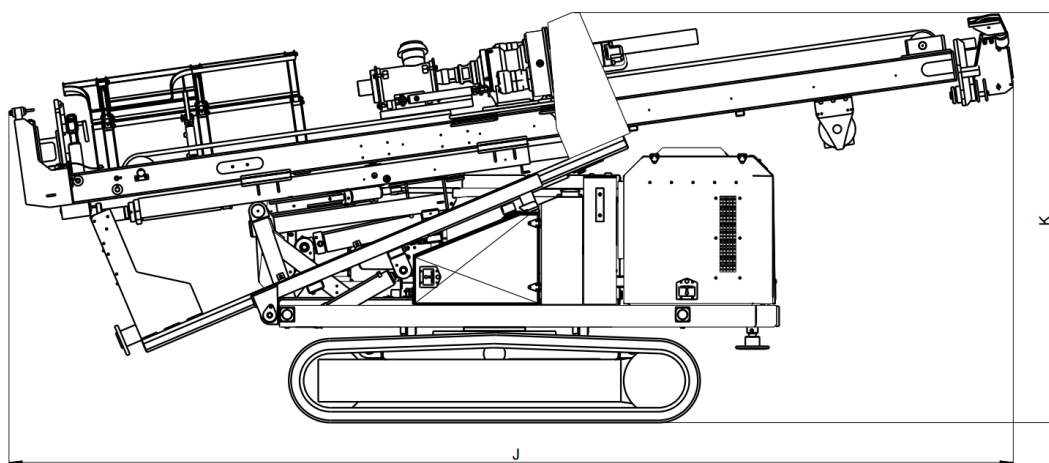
Vrtná souprava pro mikropiloty Atlas Copco WellDrill
